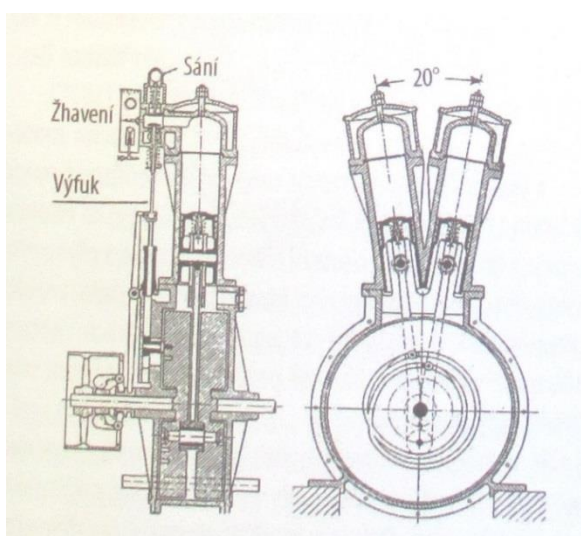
Benzínový motor Marcus – detail z roku 1888
